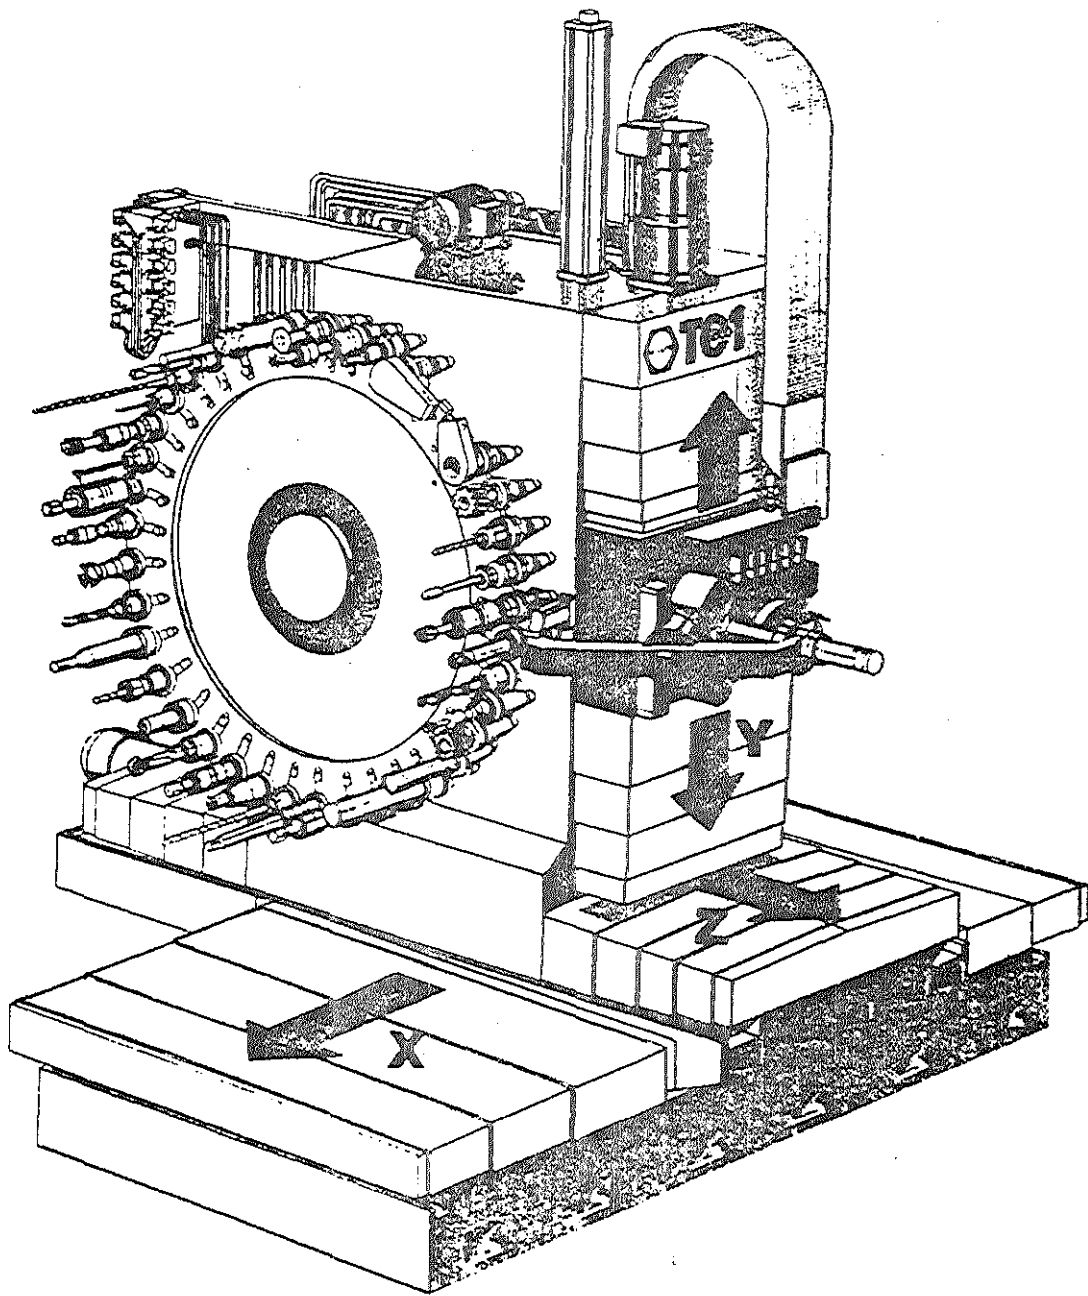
Centro de usinagem CNC horizontal com magazine de ferramentas para troca automática.
